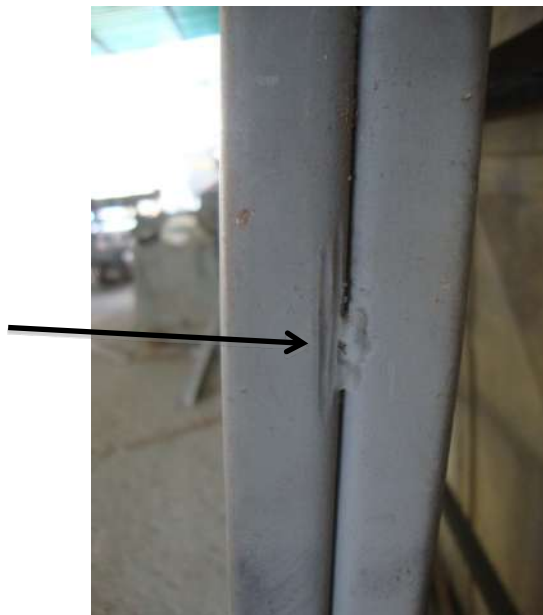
Refuerzo Tipo U Soldado
